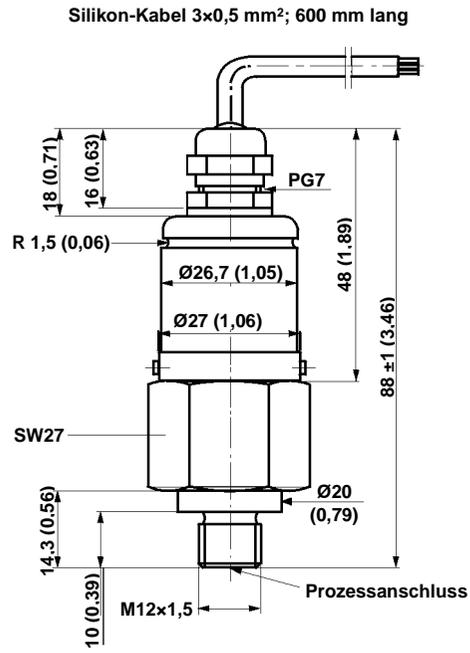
Kolben-Druckschalter Typ KD1-...-K2
